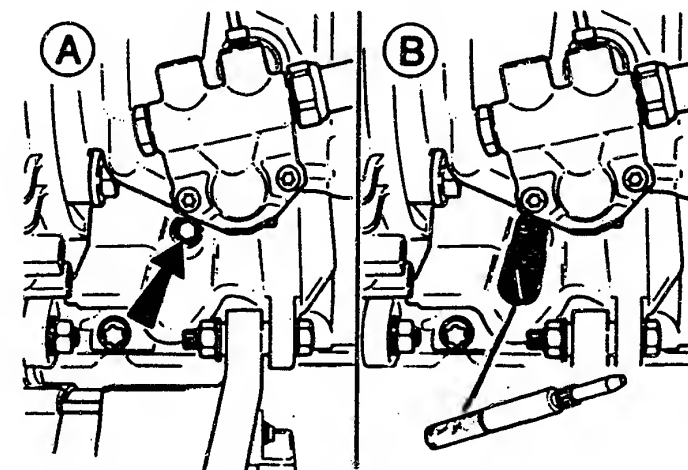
Diesel-Motor: Der Einstellstift (Spezialwerkzeug 21-104) wird anstelle der Verschlusschraube (Pfeil in A) eingesetzt. Sobald die Kurbelwange in Lafrichtung am Stift ansteht, steht der Motor in der OT-Position des 1. Zylinders.
